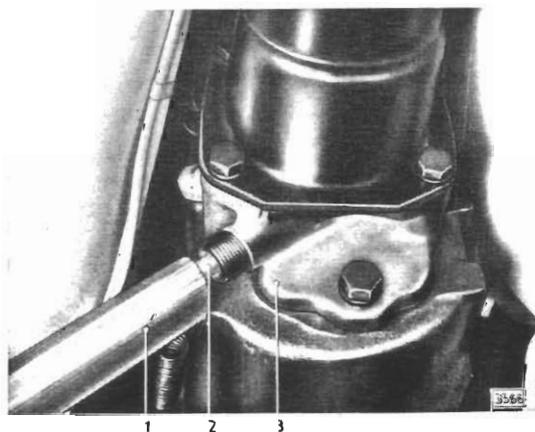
Schlankes Holzstück an Tachometerschraubenrad ansetzen
